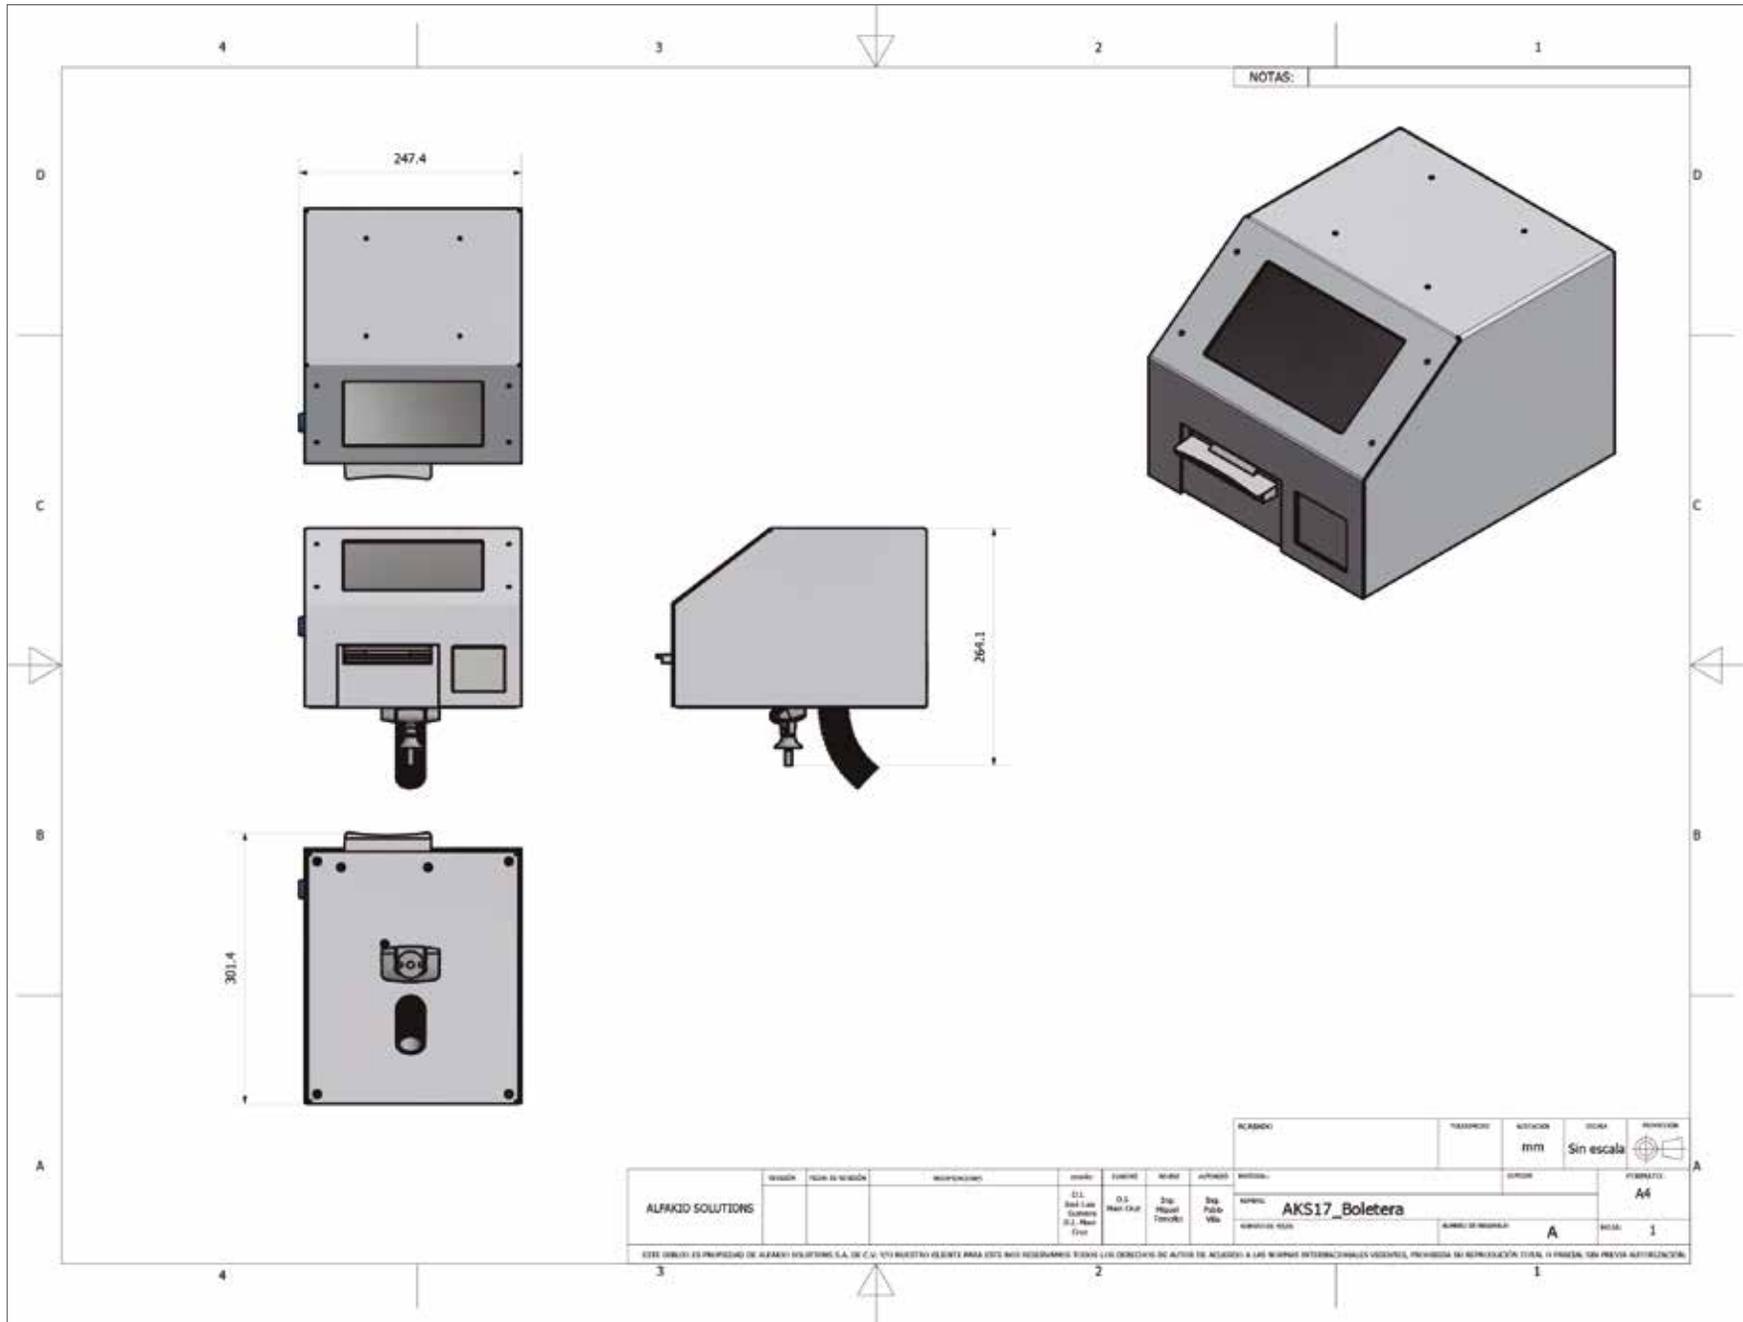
Haz terminado de instalar la envoltura de boletera. Fuente propia.
